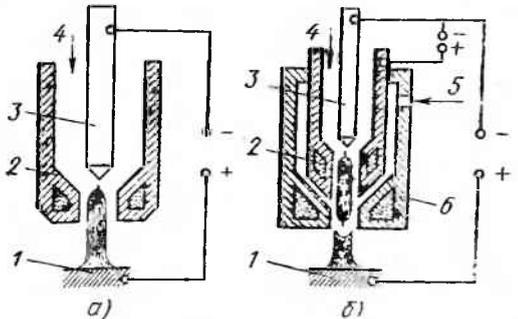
Схемы горелок для плазменной резки: а — горелка прямого действия, б — горелка комбинированного типа; 1 — заготовка, 2 — охлаждаемое сопло, 3 — вольфрамовый электрод, 4 — плазмообразующий газ, 5 — стабилизирующий газ, 6 — внешнее охлаждаемое сопло
